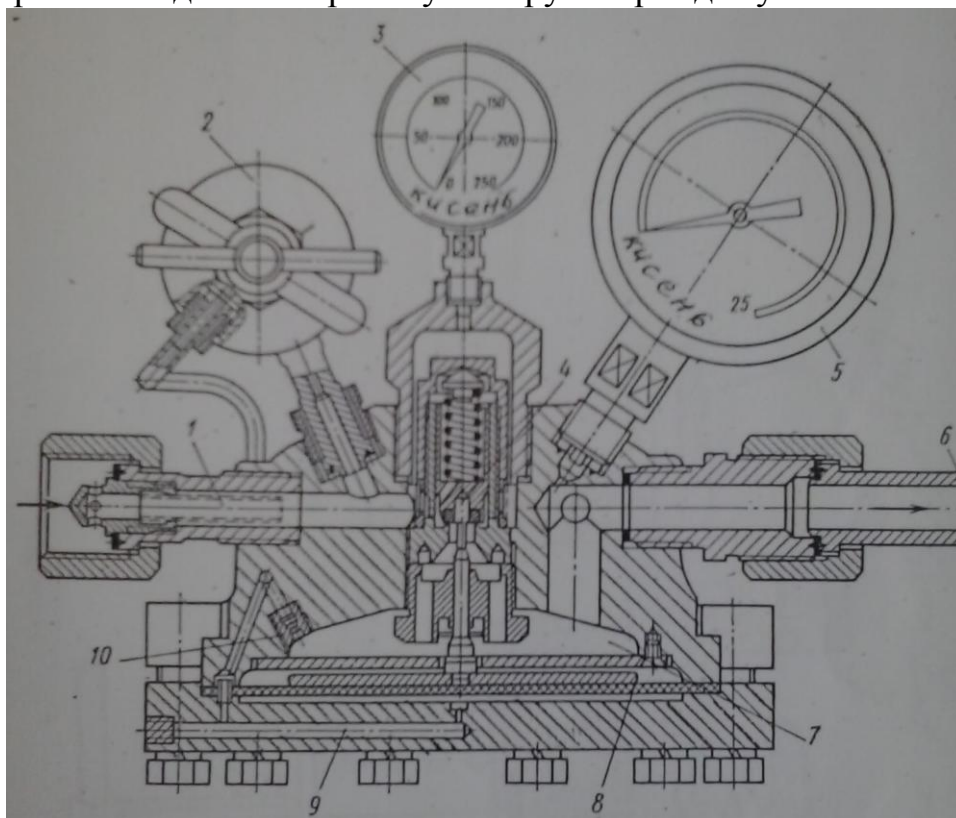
Рамповий редуктор ДКР 250/500 з пневматичним регулятором величини робочого тиску
